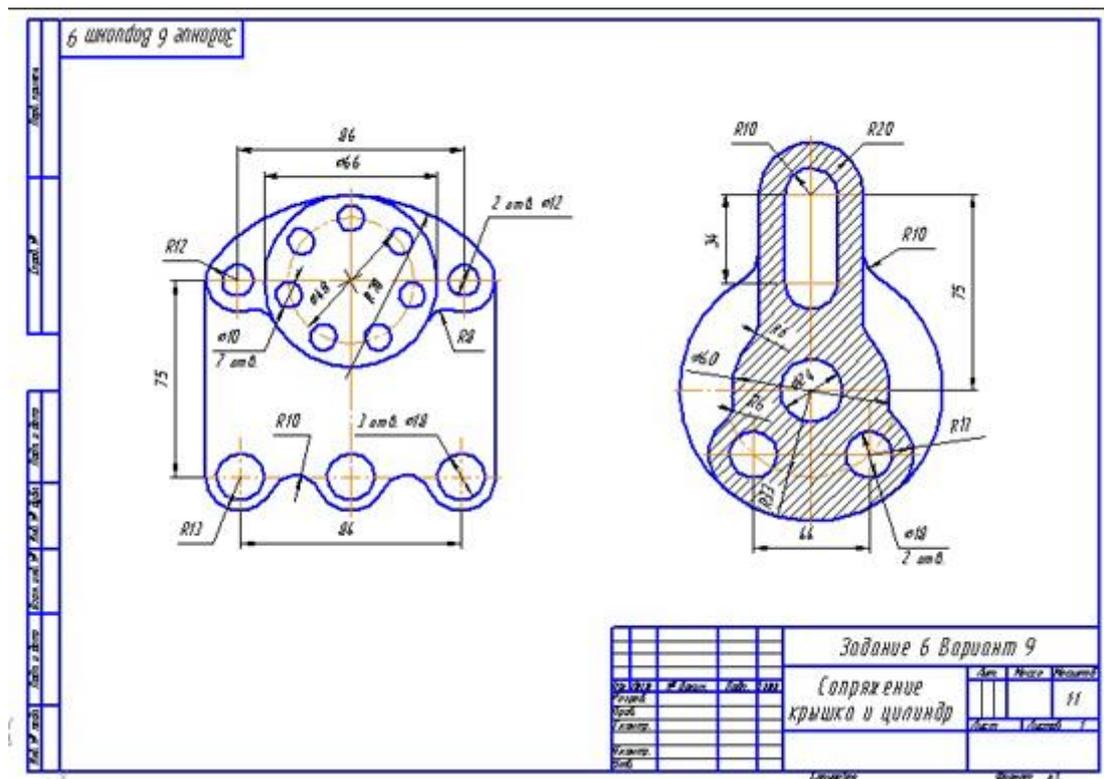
Сложный чертеж – сопряжение крышка и цилиндр
